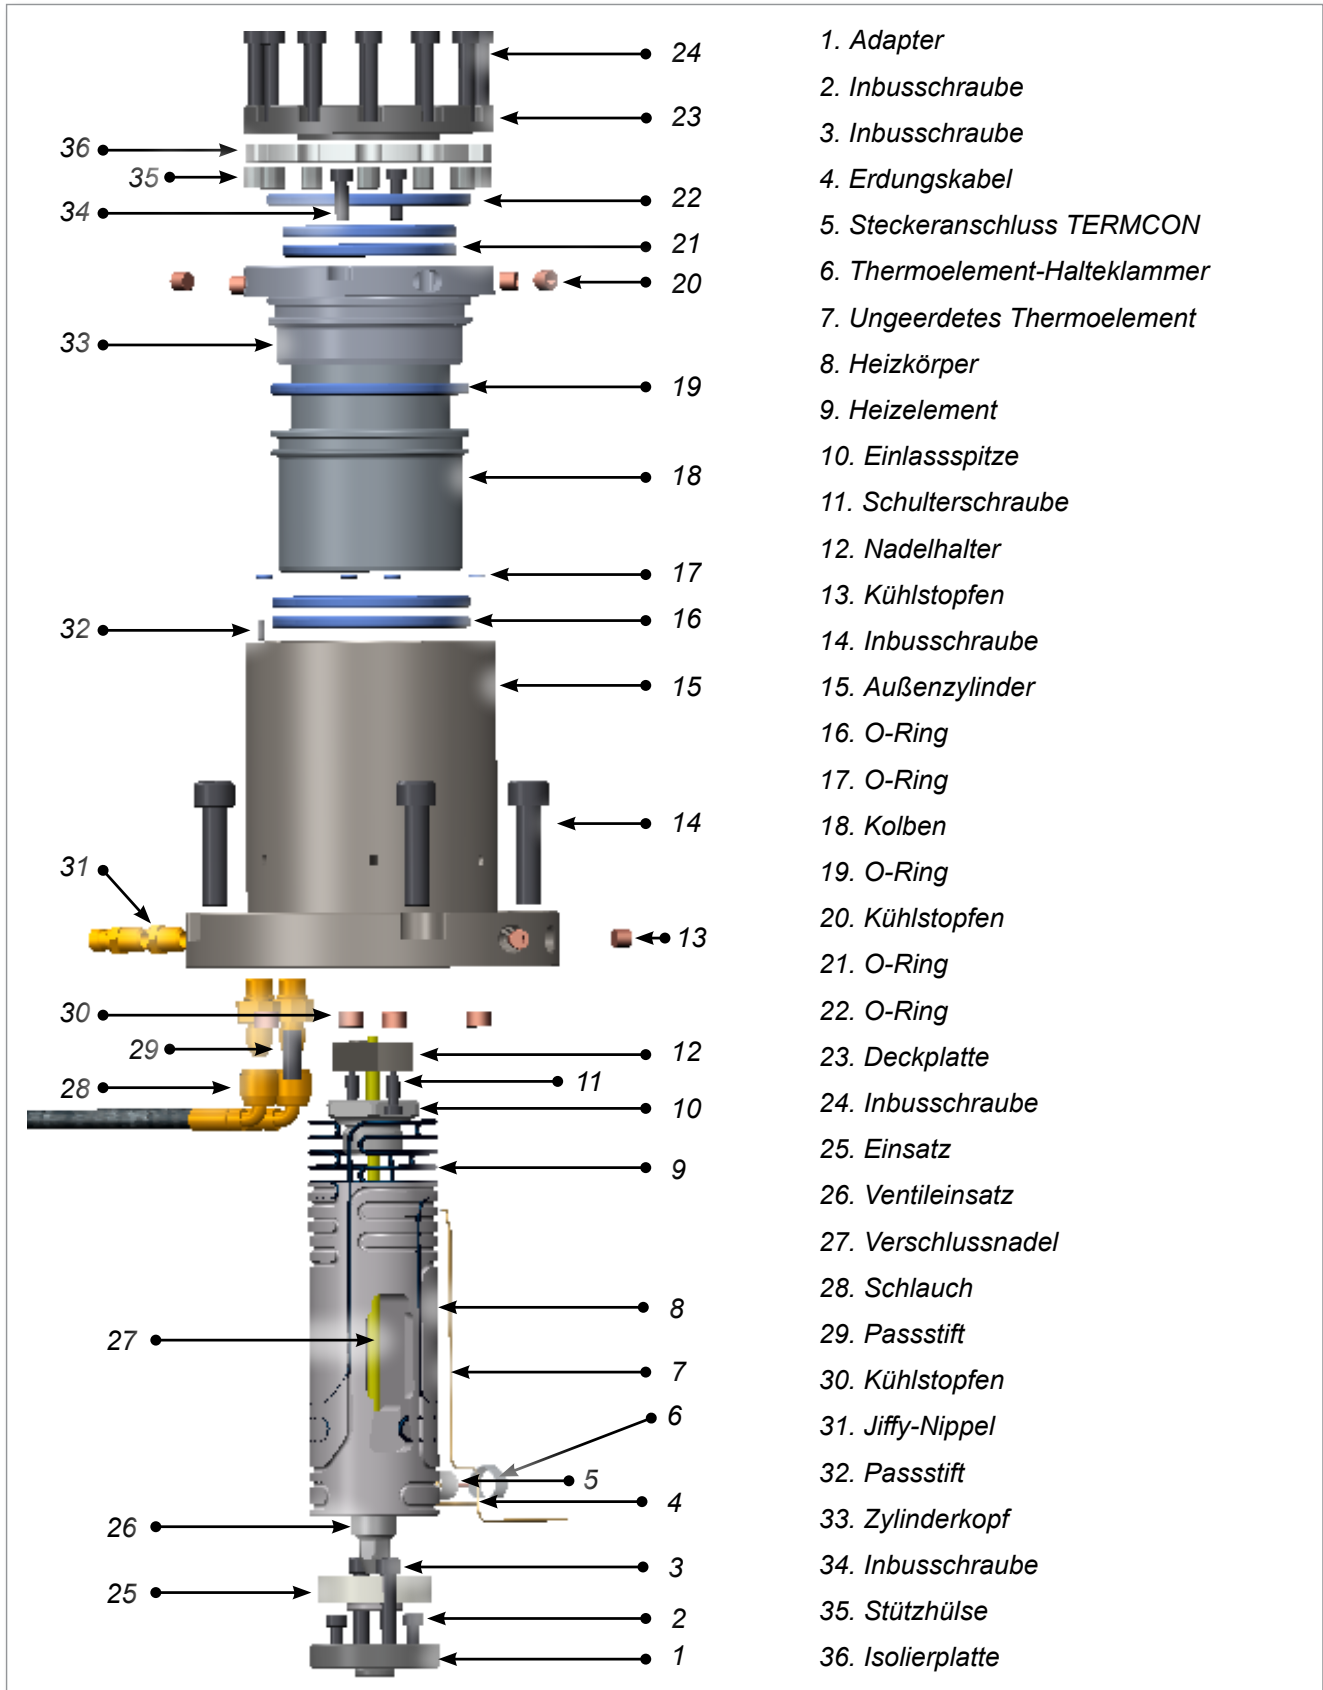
Accu-Line™ Gehäusebaugruppe
